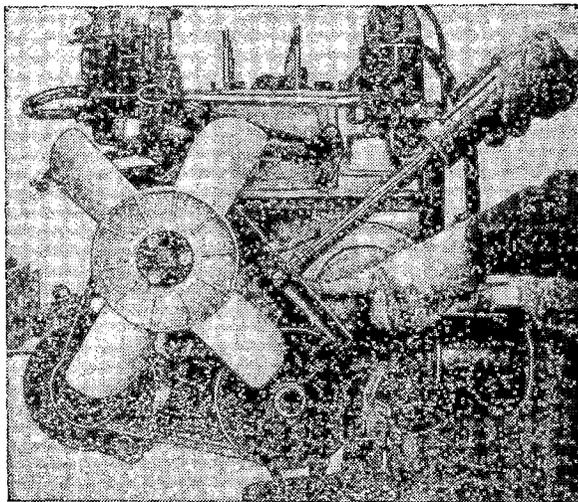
Проверка натяжения ремня привода вентилятора динамометром КИ-8920
